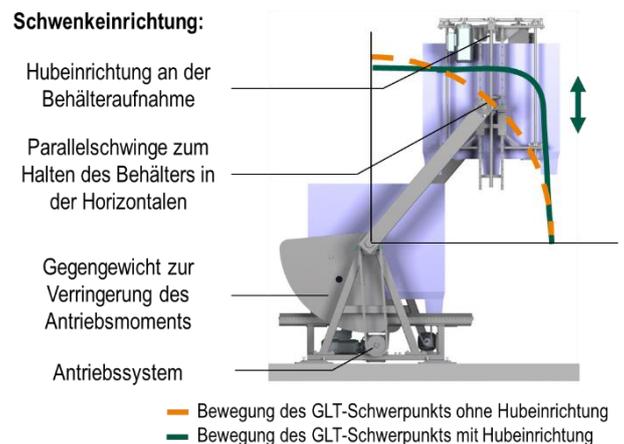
Schwenksystem des GLT-Wechslers (CAD-Capture)
